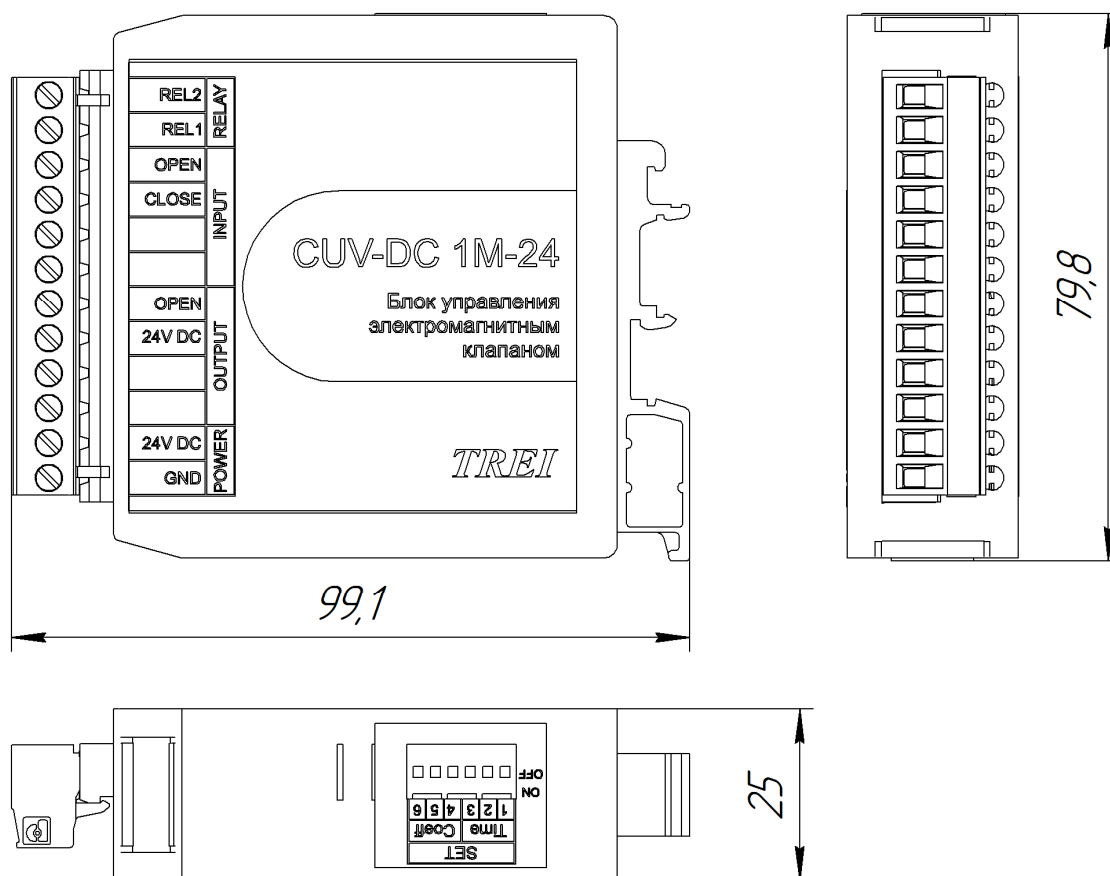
Чертеж общего вида CUV-DC 1M-24 с указанием габаритных и присоединительных размеров
